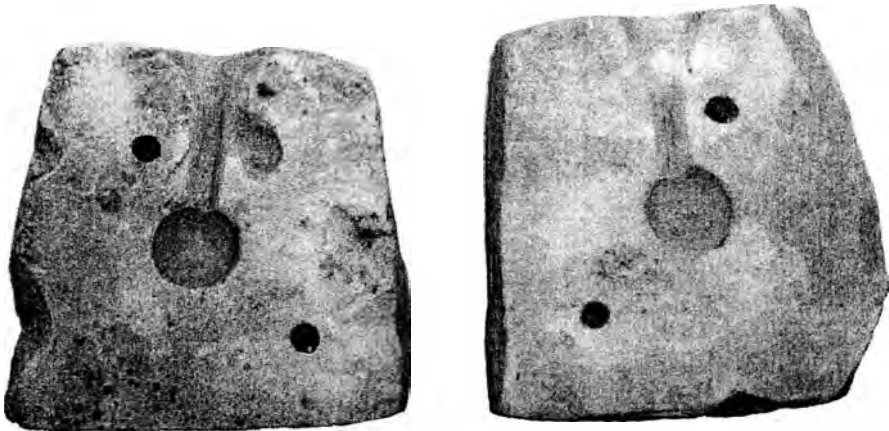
Створки формы для отливки пуль калибром 14 мм.
